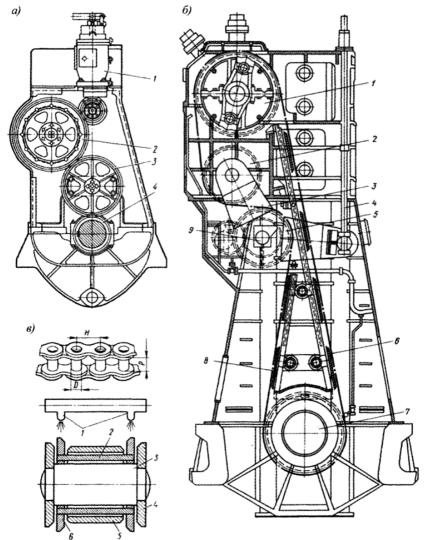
Цепной привод распределительного вала 2-тактного двигателя находится в зацеплении с ведущей шестерней 4 коленчатого вала и с ведомой шестерней 2 распределительного вала.
